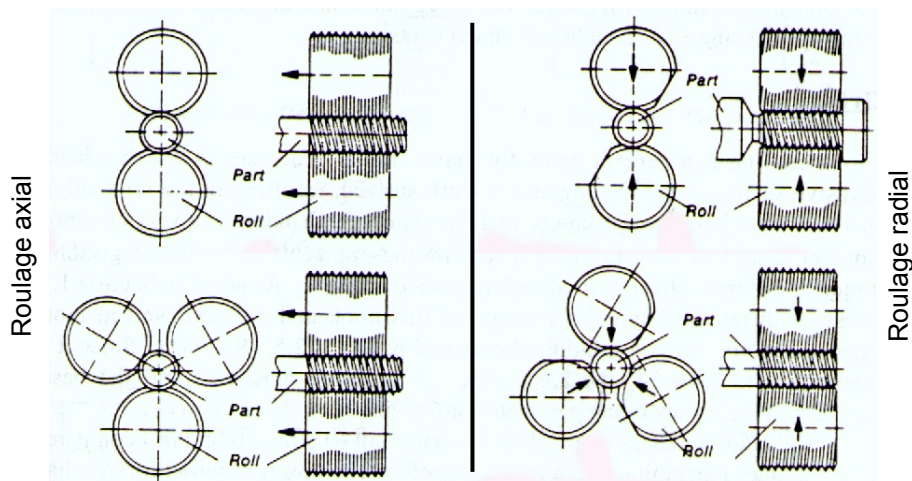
Roulage extérieur axial ou radial, à 2 ou 3 molettes [MetCut].
